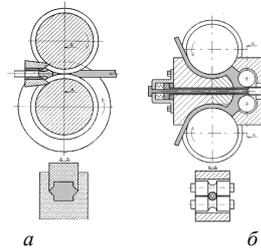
Устройства для получения сварных труб (а) и длинномерных полых изделий (б)
